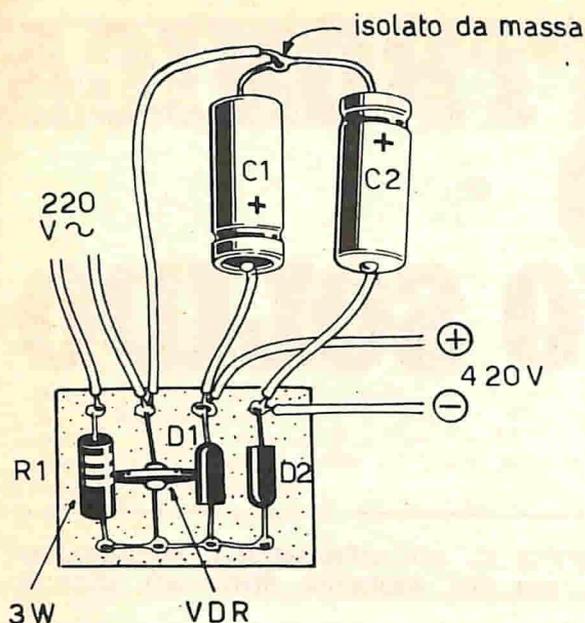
Ecco il piano di cablaggio del circuito duplicatore di tensione rappresentato in figura 1. Componenti: C1 = C2 = 100 μ F - 350 VI.; VDR = Philips 2322 555 03541; D1 = D2 = BY127; R1 = 10 ohm - 3 W.
